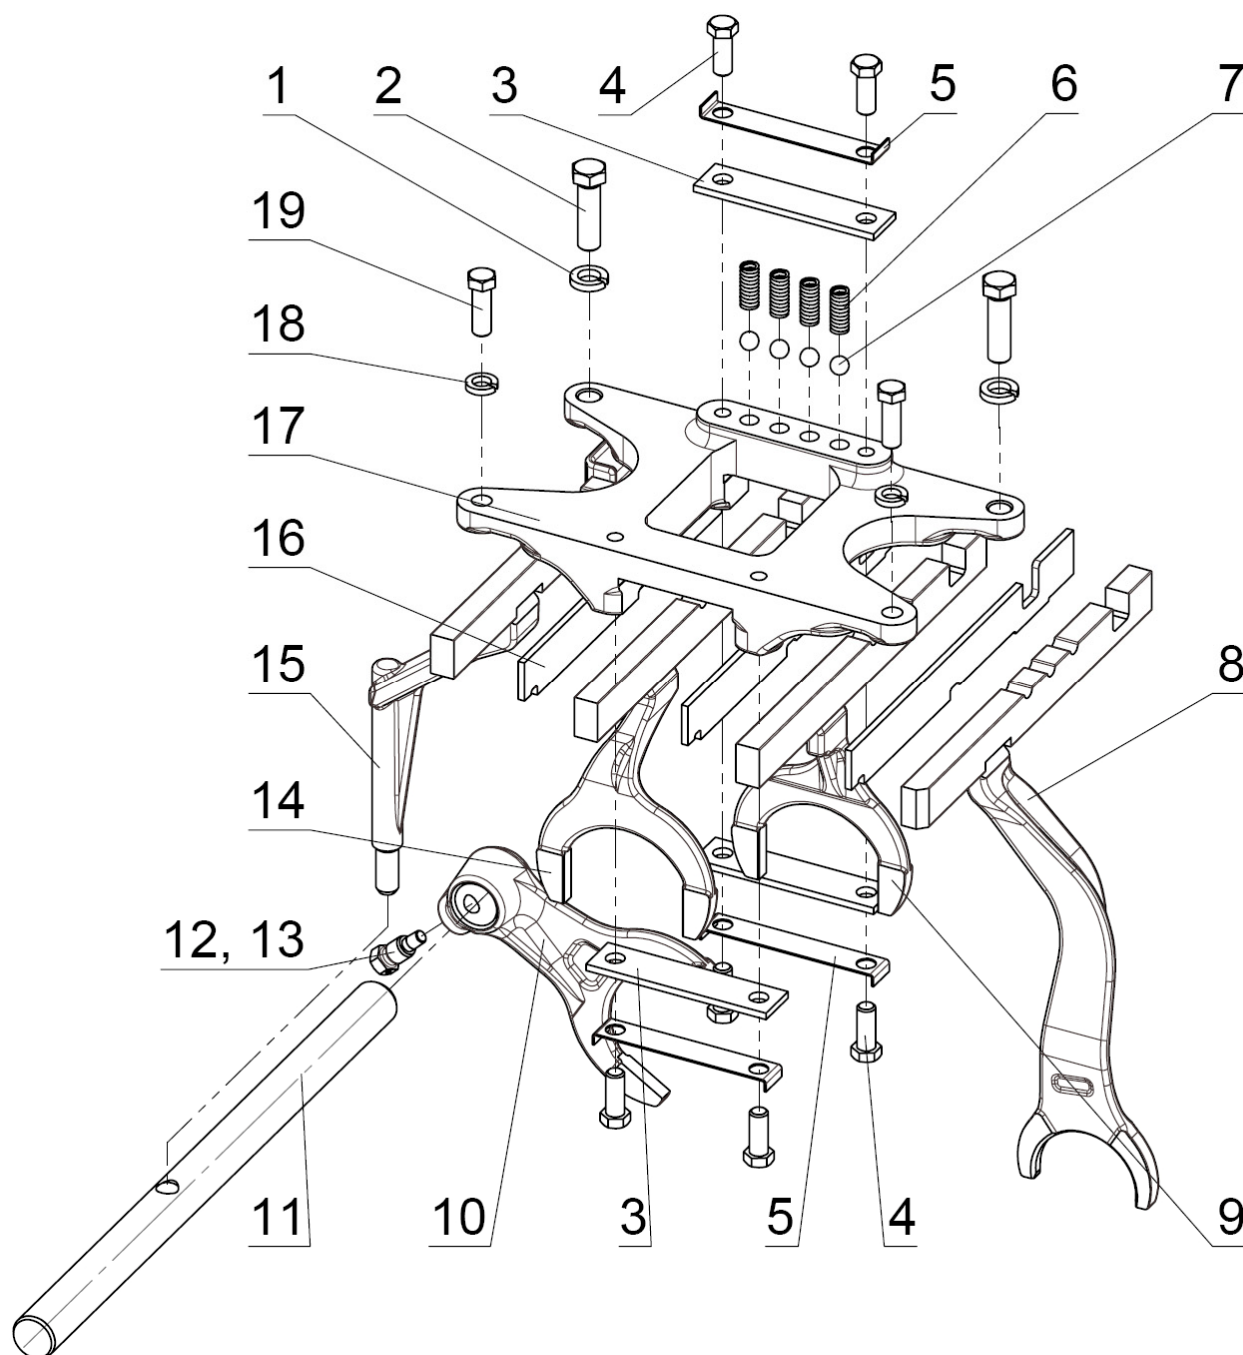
Корпус вилок механической КП. Корпус вилок
